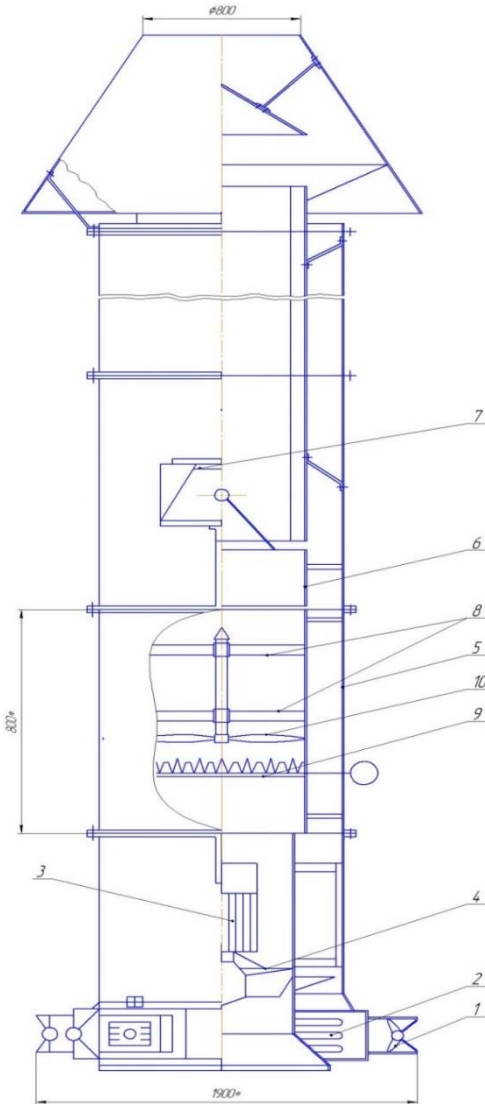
Модернизированная приточно-вытяжная установка.
